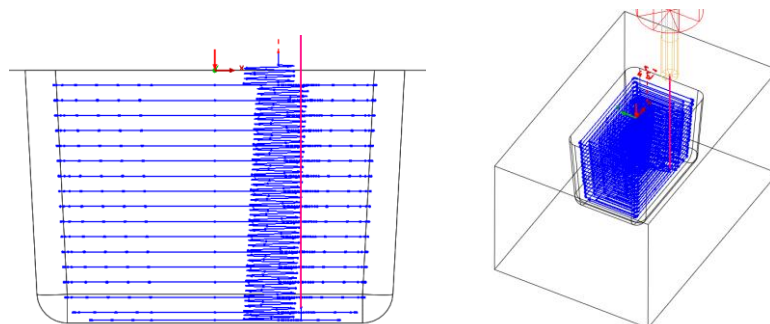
Траєкторія руху інструменту при чорновому фрезеруванні призматичного заглиблення
